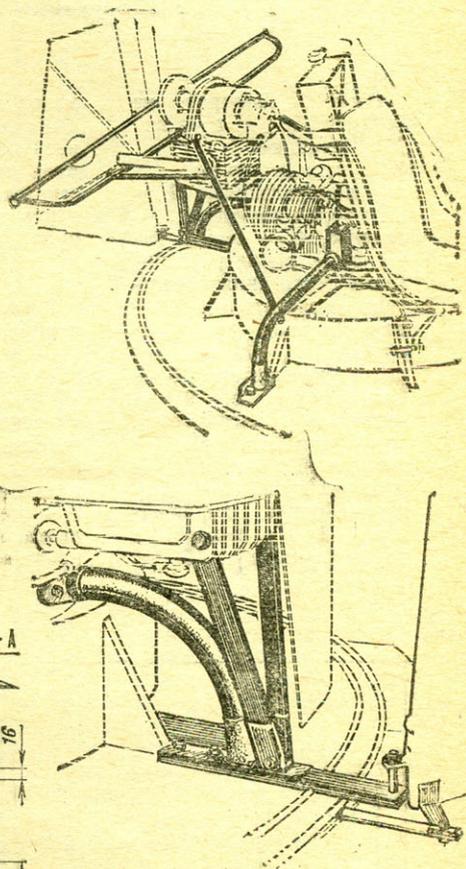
Крепление двигателей и подвеска руля направления (поворота).
